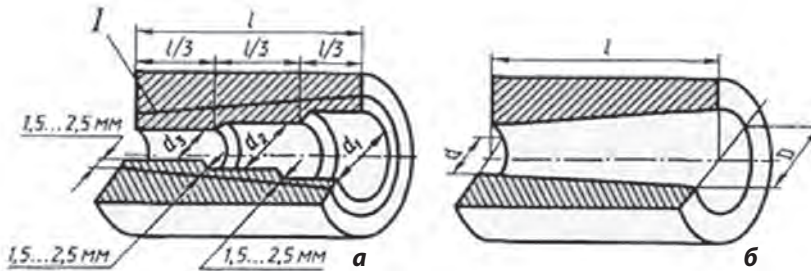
Попередня обробка під розточування конічного отвору:
